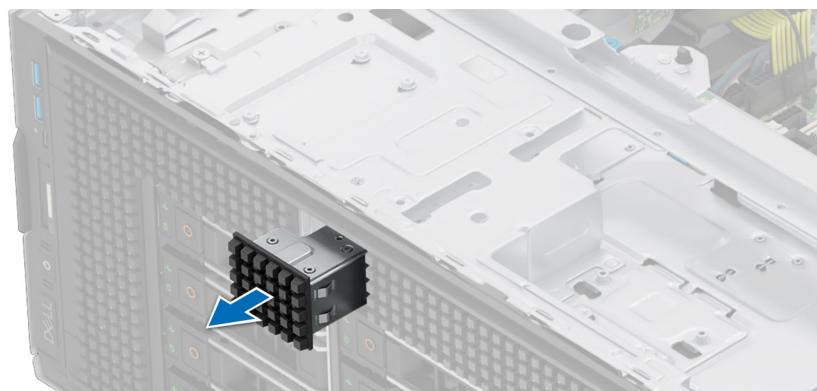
Entfernen des Platzhalters für das BOSS-N1-Modul
